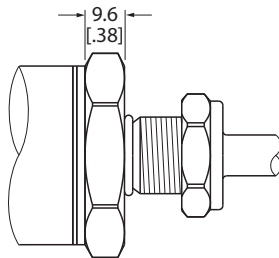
Ausführung mit Flat Face (F10) – Gehäusemutter mit Gewinde
